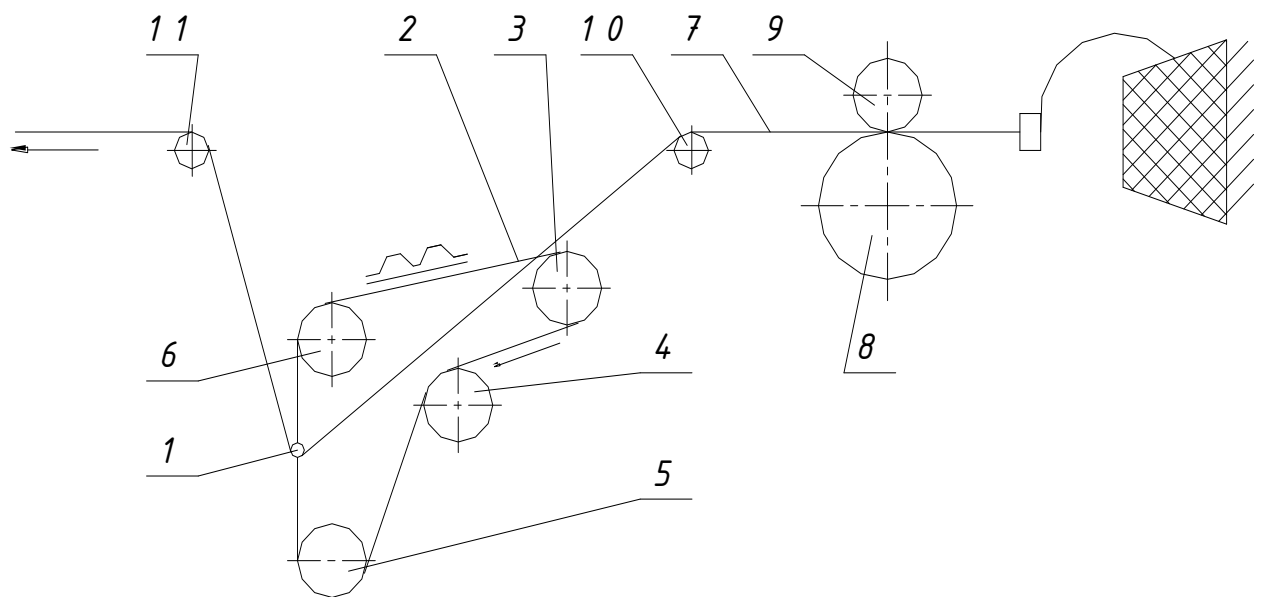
Механізм компенсації уточної нитки з чотирма зубчатыми колесами
